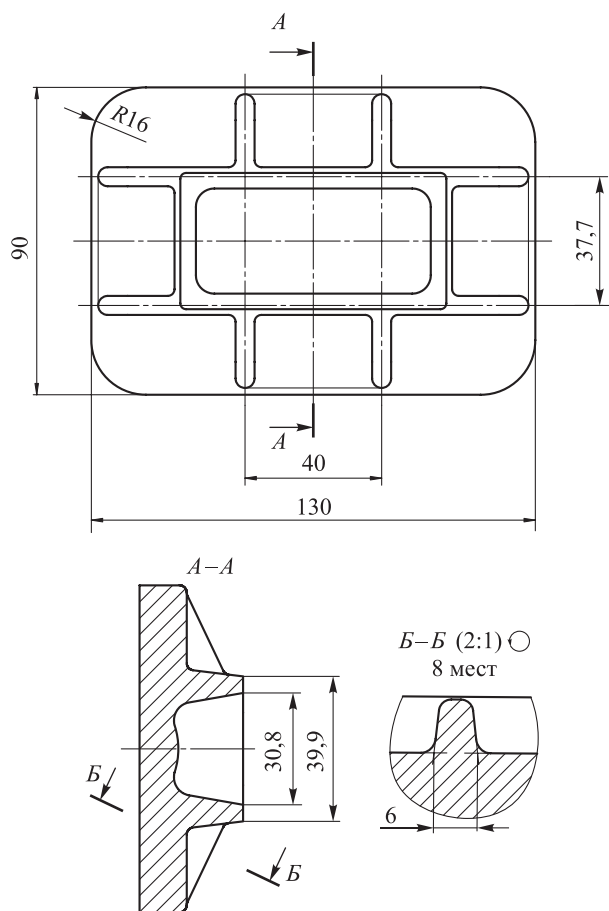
Эскиз получаемой поковки фланца с основными размерами
